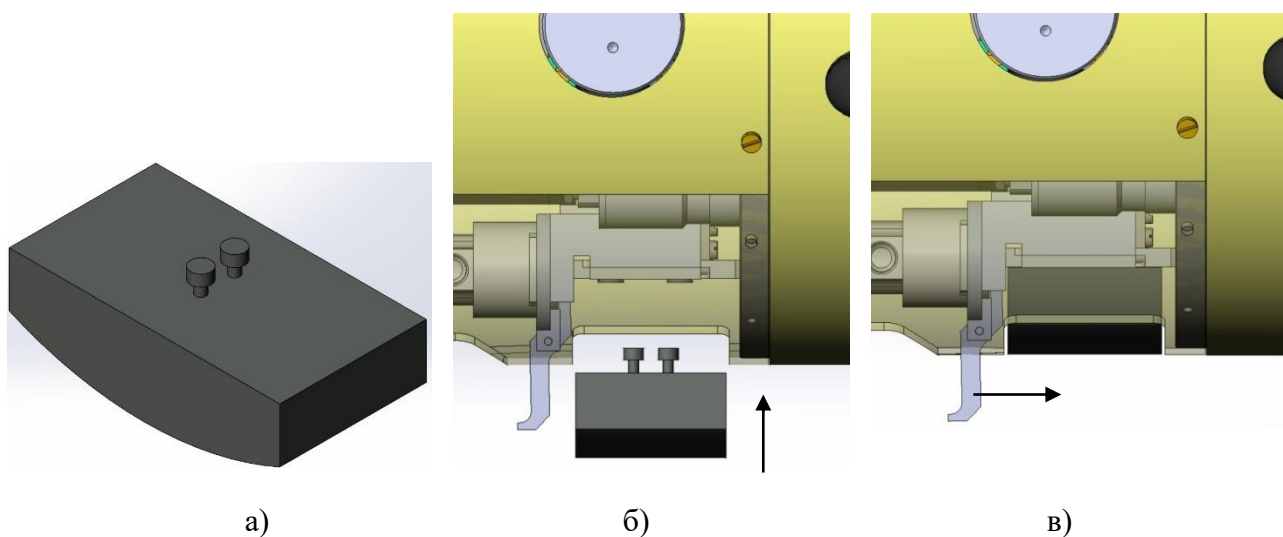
Аварийный балласт а), установка аварийного балласта б), в)
